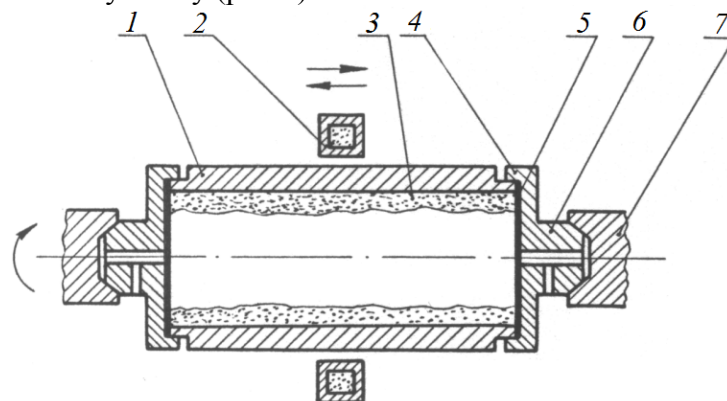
Схема нанесення евтектичного покриття на внутрішню поверхню циліндричної деталі з використанням нагрівання СВЧ: 1 – стальна втулка; 2 – індуктор; 3 – шхта; 4 – фланець;
